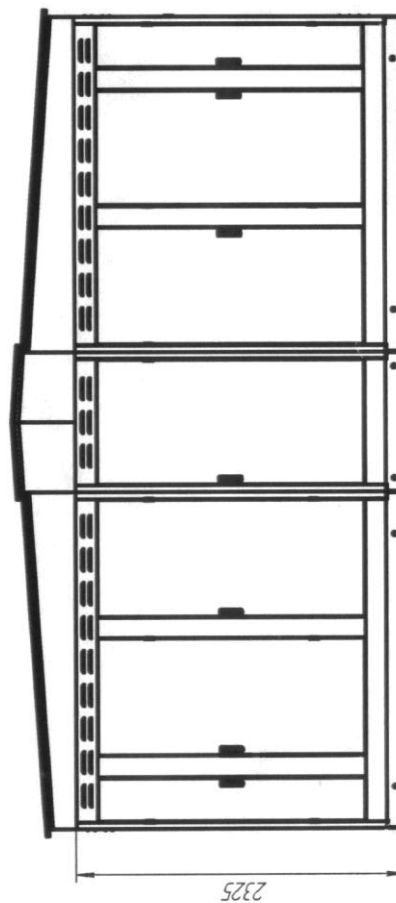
Габаритные и установочные размеры 2КТПН-Орб 07
